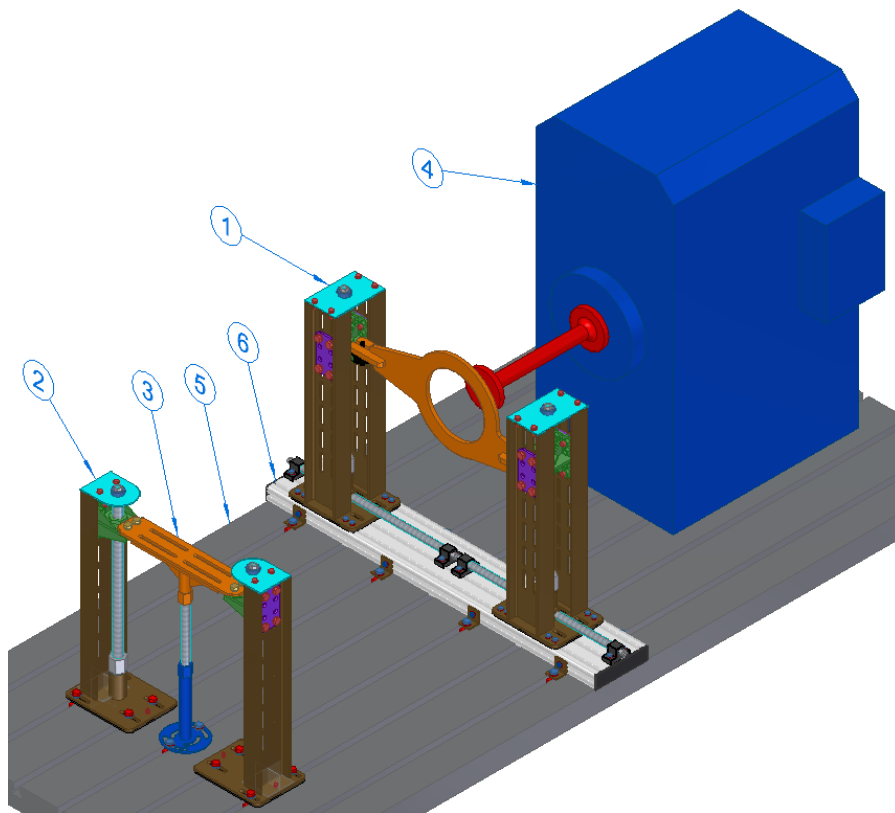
3D model modulárního stojanu bez vodorovné regulace. 1 - přední stojan; 2 - zadní stojan; 3 - podélník a vzpěra; 4 - dynamometr; 5 - základová deska
